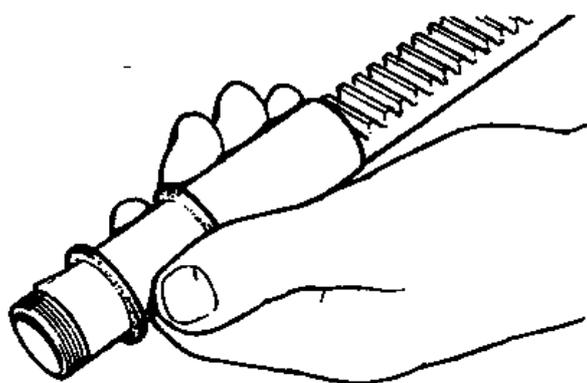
При установке манжет пользуйтесь защитной фольгой (Разд.35)
